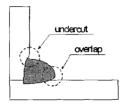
용접 결함 정의 Fig. 3 welding defects: undercut and overlap
